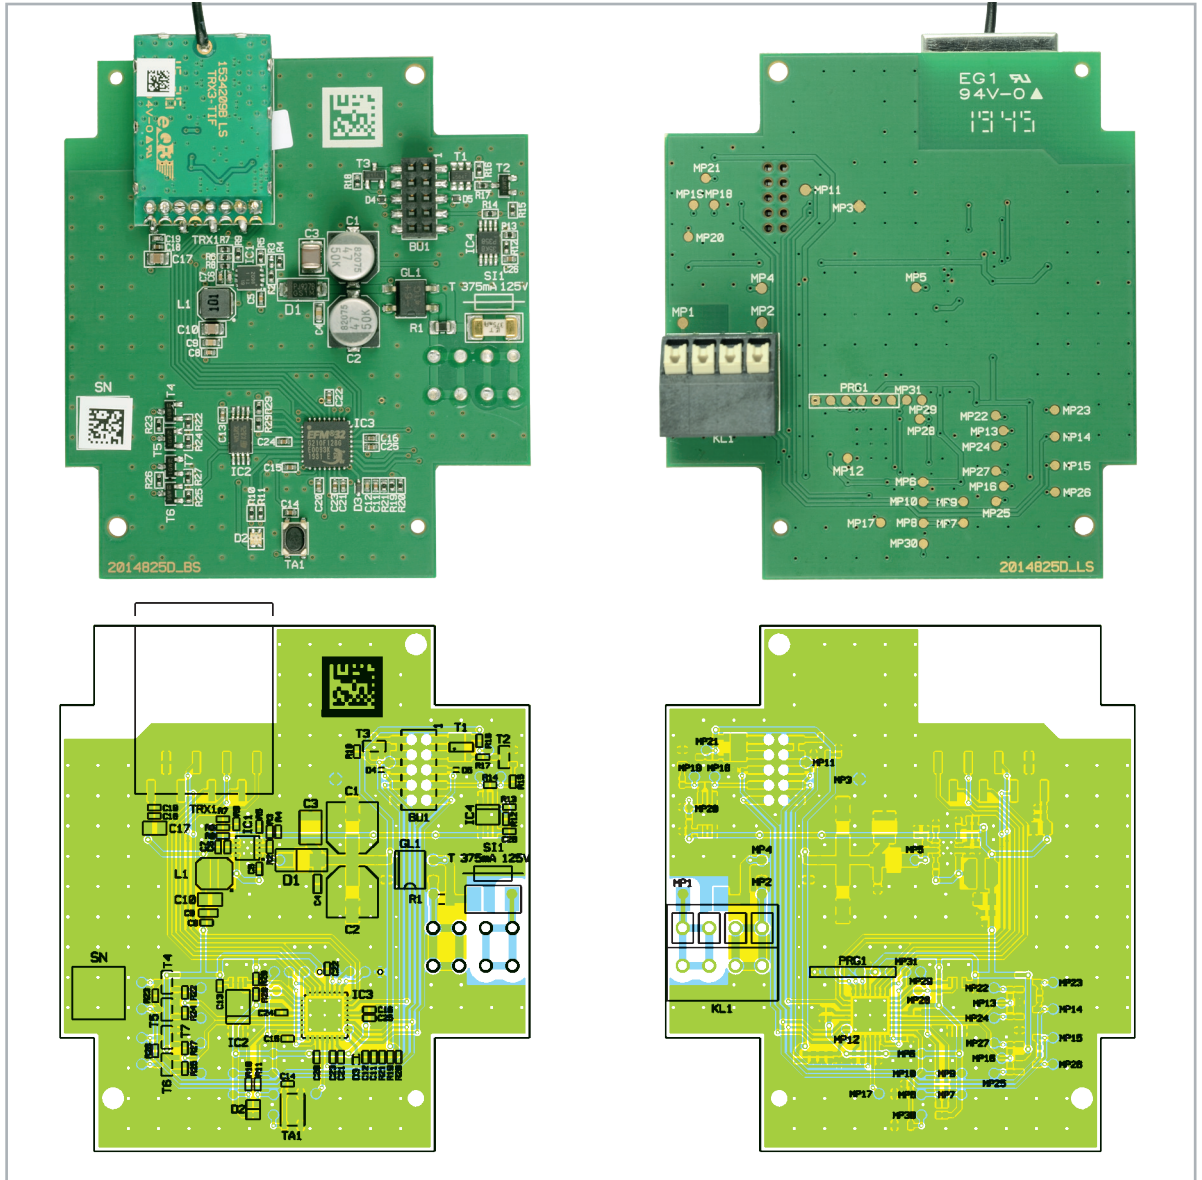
Die Platinenfotos der komplett bestückten Hauptplatine, darunter die zugehörigen Bestückungspläne
